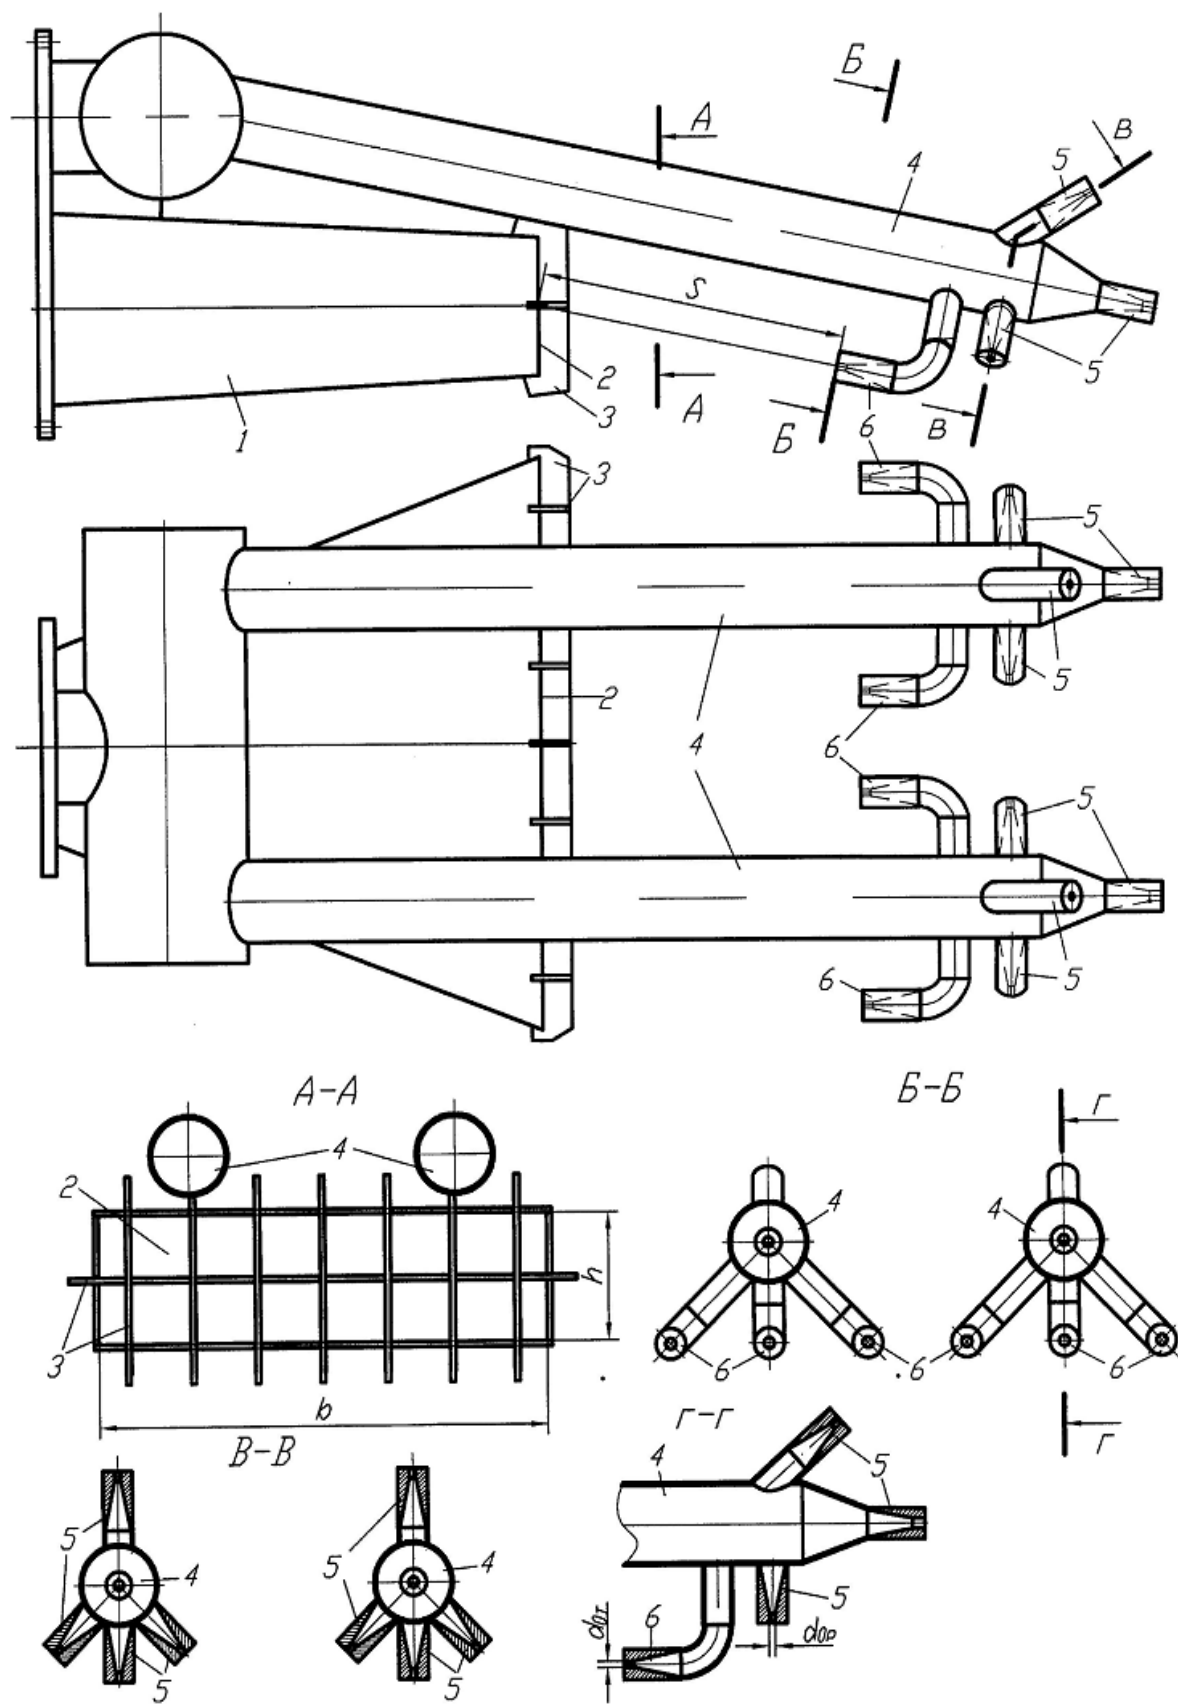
Схема двухмониторного грунтоприемника с принудительным подводом грунта
